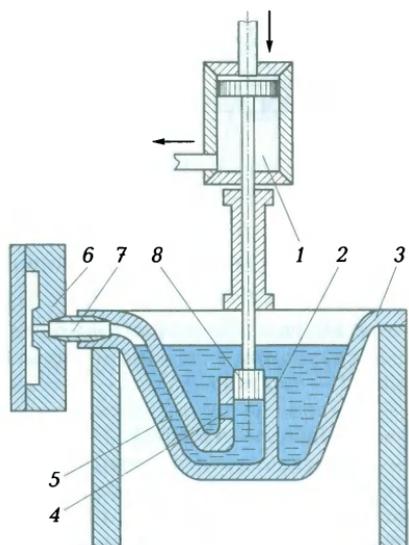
Схема поршневой машины с горячей камерой прессования:
